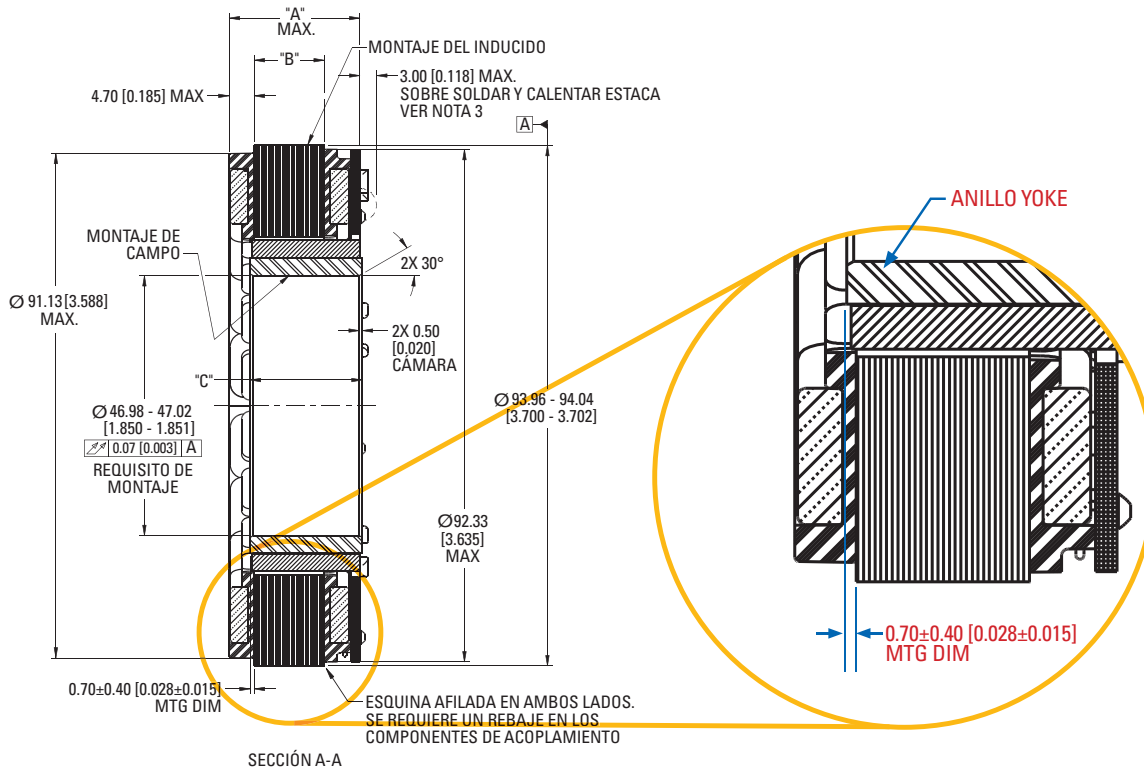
Ilustración de dimensiones de montaje mostradas en un diagrama TBM2G-068XXX-XXXX-00. Esta dimensión se mide desde el borde izquierdo de la pila de laminado hasta el borde izquierdo del material del yugo (no magnético).
